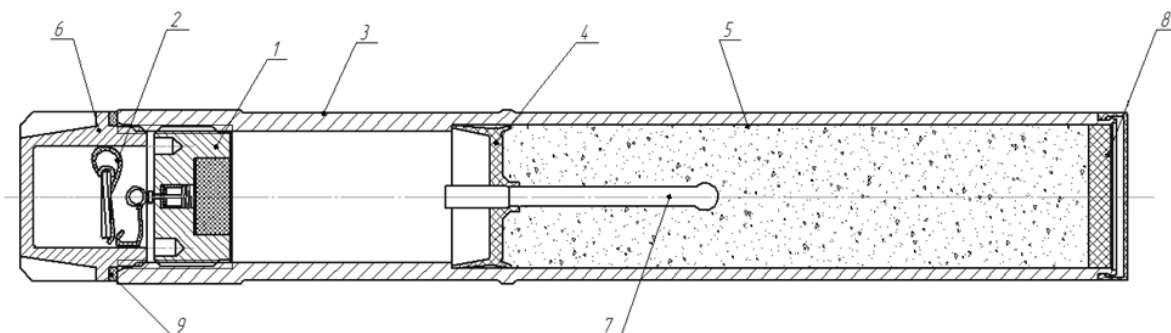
Устройство огнетушителя «Малыш»: 1 – дно с терочным приводом; 2 – фал; 3 – корпус; 4 – поршень; 5 – порошок; 6 – крышка; 7 – трубка; 8 – пробка с колпачком; 9 – прокладка
